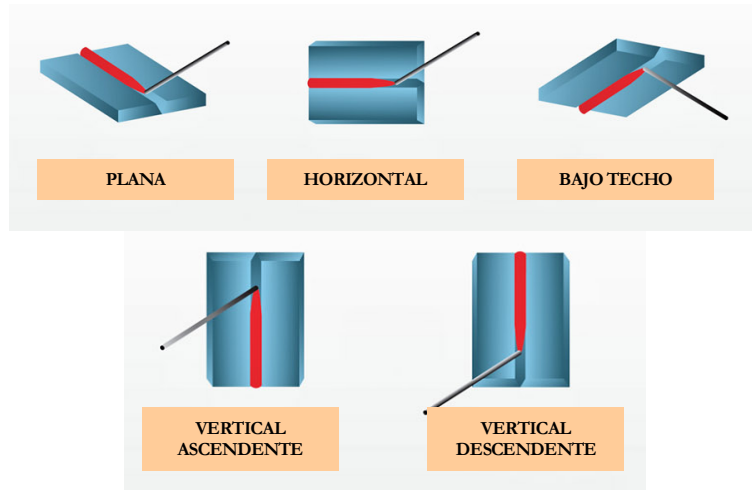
Posiciones de realización de una soldadura [21].
